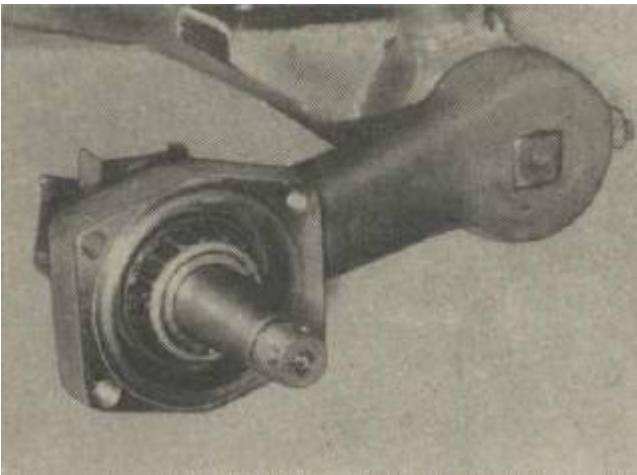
Eingedrücktes hinteres Kegelrollenlager
